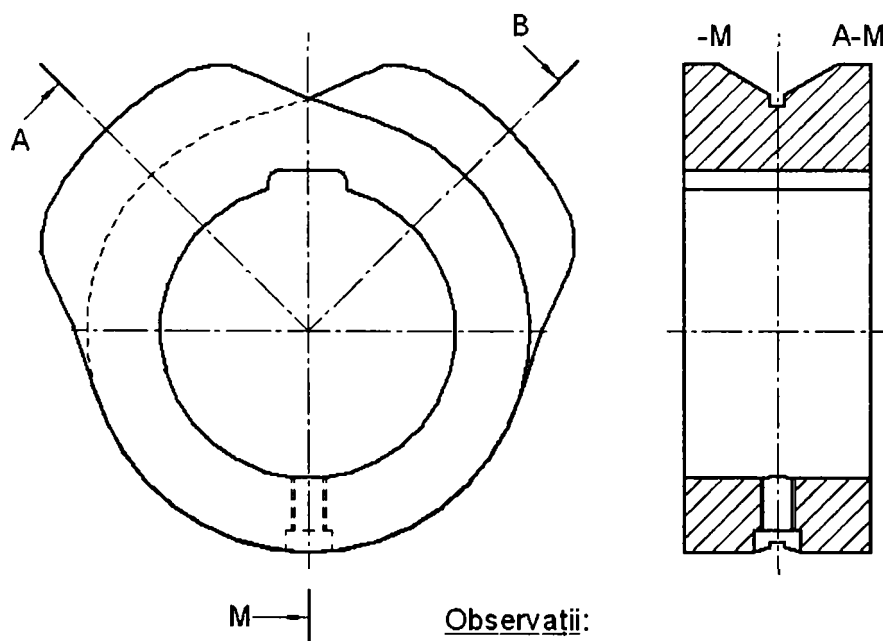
Cama de injecție a motorului Diesel MAN , tip KSZ 90/160A
